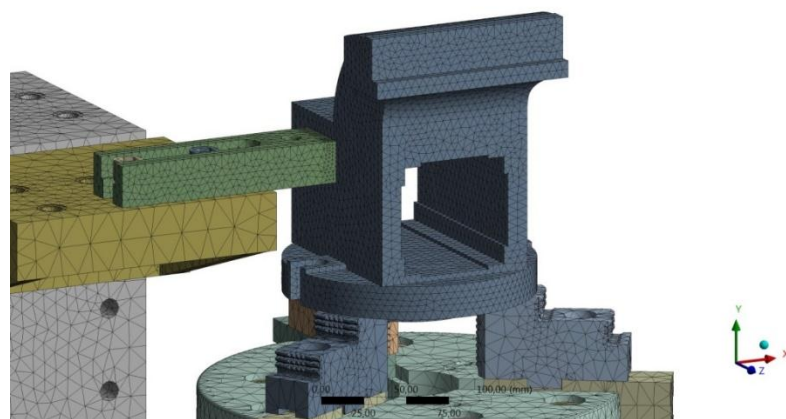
Конечно-элементная модель конструкции переналаживаемого приспособления с обрабатываемой деталью в расчетной системе ANSYS®Mechanical
